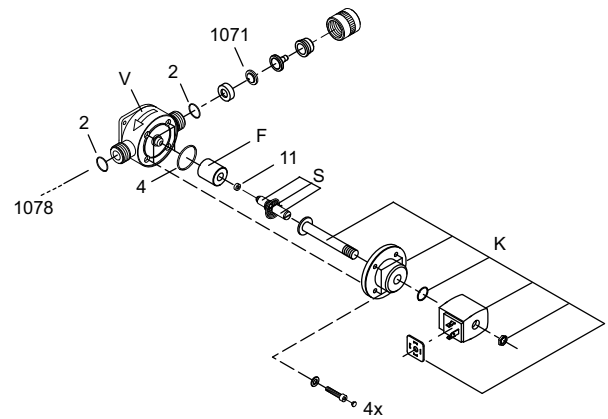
ЭМК (OCD-162-5, -10): Сборочный чертёж
